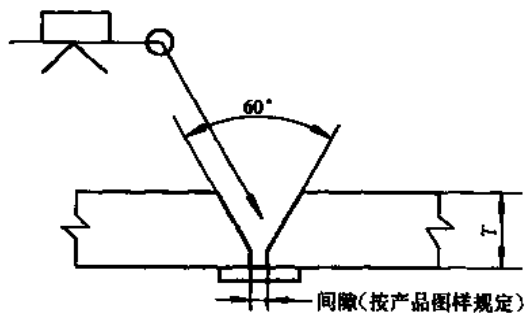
带衬垫管材对接接头焊接工艺评定试件形式和尺寸
